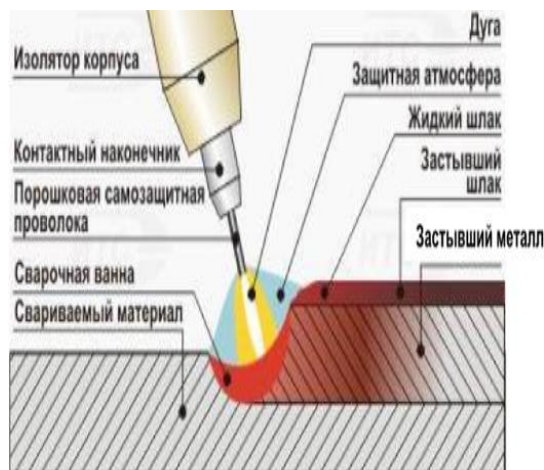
Эскиз механизированной сварки с порошковой проволокой
